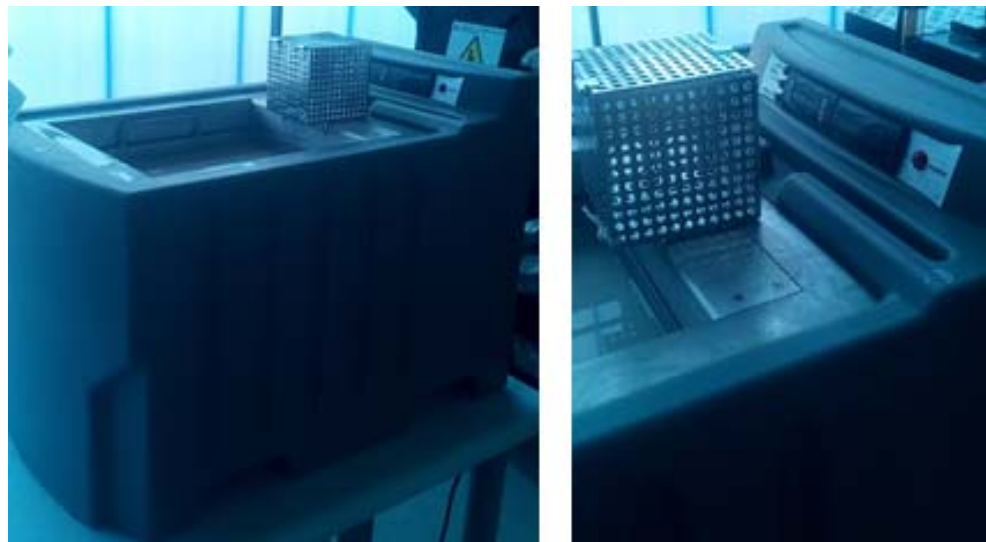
141. Máquina para remoción de material de soporte. (Fuente: Autor)
